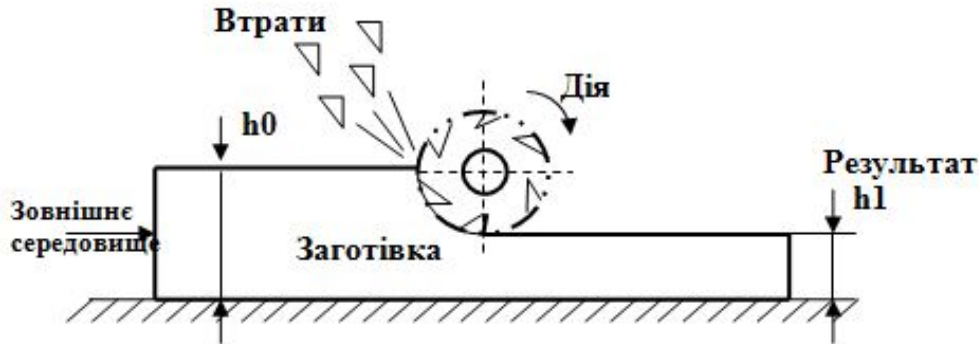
Схема зміни заготовки в оброблювальному верстаті
